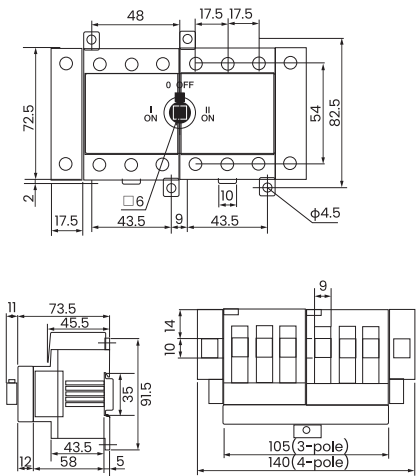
Габаритные и установочные размеры реверсивных рубильников 63-80А 3Р-4Р
